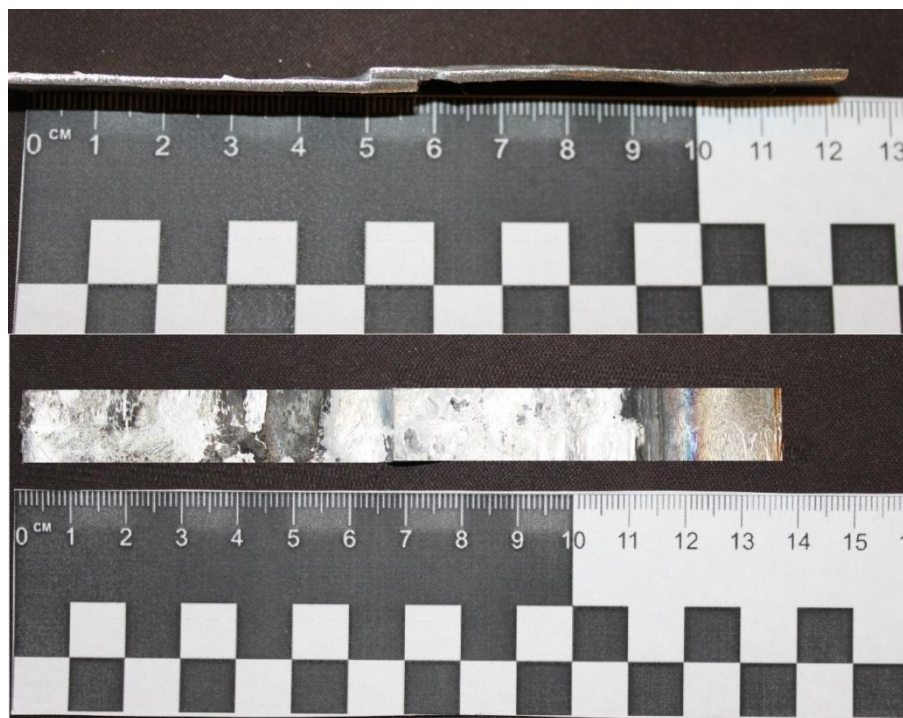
Внешний вид образца для механических испытаний на отрыв
